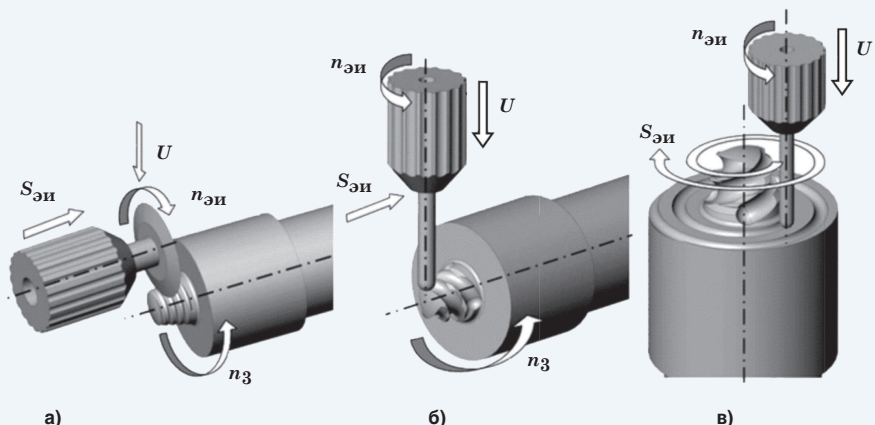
Технологические схемы формообразования геометрии инструмента для сварки трением-перемешиванием: а) формирование малой винтовой канавки, б) формирование на пине винтовой канавки стержневым электродом; в) формирование винтовой канавки на бурте инструмента
